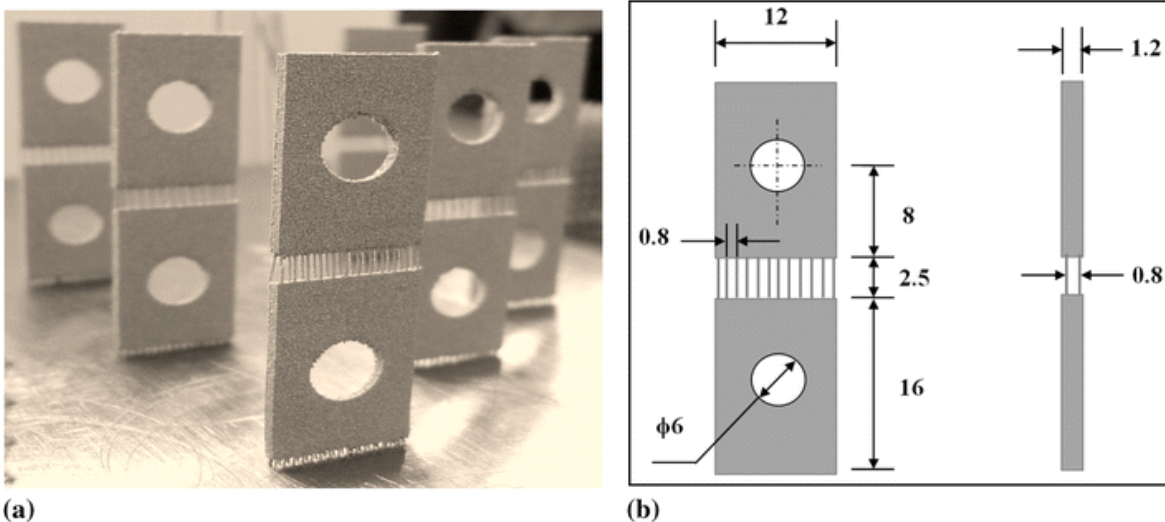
Kombinované prutové těleso pro tahovou zkoušku
